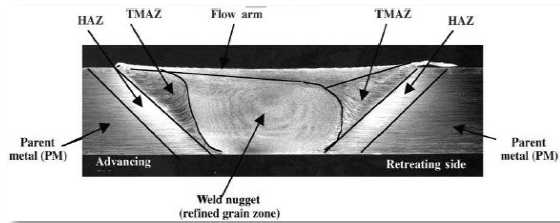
Heat zone pada friction stir welding [Mishra 2007]
